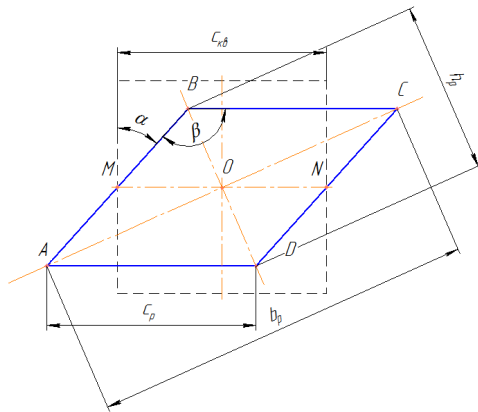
Схема взаимодействия задаваемой квадратной заготовки с ромбическим калибром
